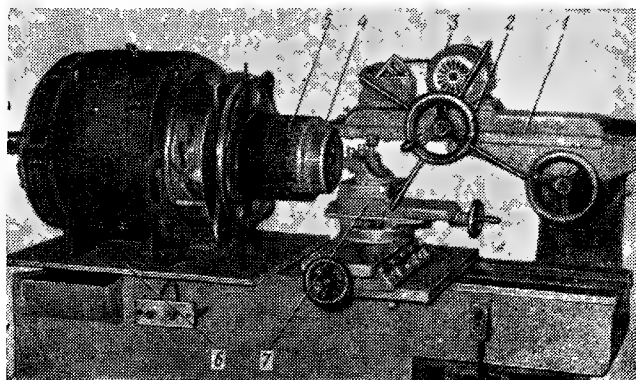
Станок для продорожки и проточки коллектора генератора управления ДК-405 после посадки на вал двигателя:
